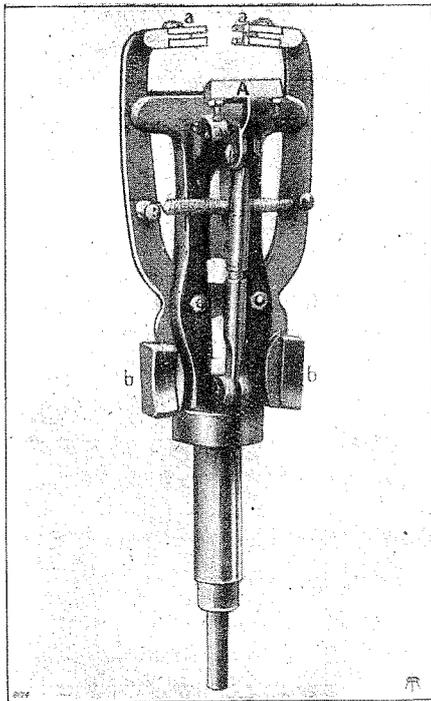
Détail d'un des supports *a* de la machine fig. 8.
